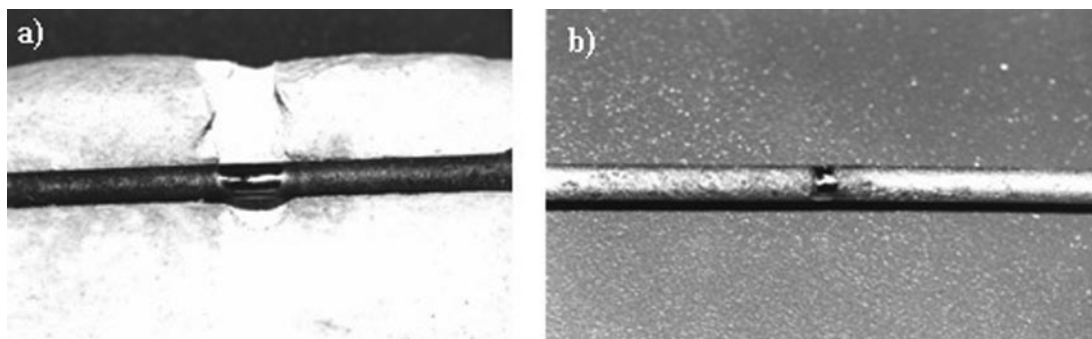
Corpos-de-prova. a) Solda TIG. b) Solda Laser.
